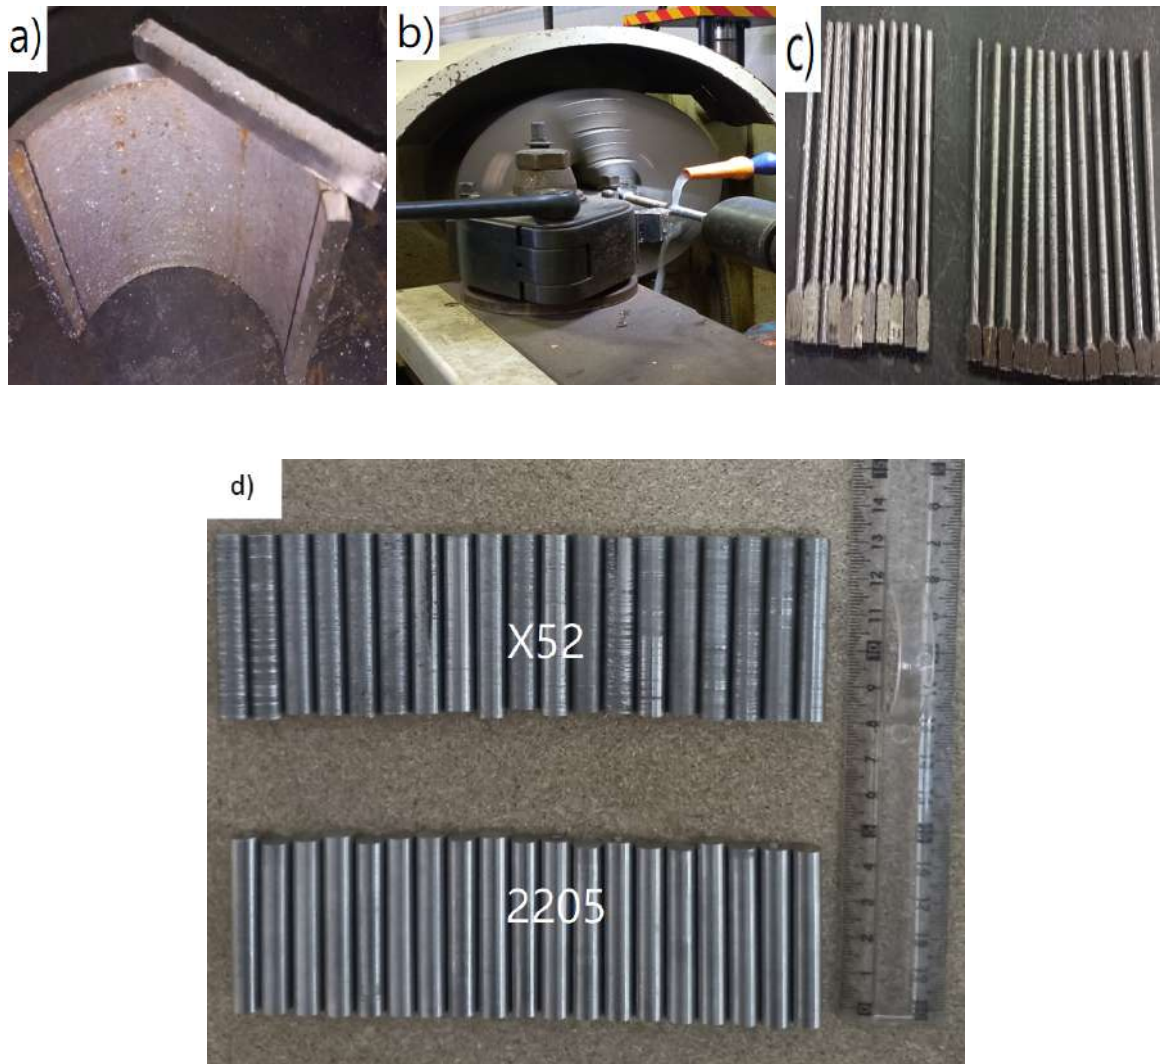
Étape de préparation des échantillons a) Segment du métal de base découpé à partir d'un tube pipelines, b,c) Chariotage des segments, d) Matériaux prêt pour le soudage.
